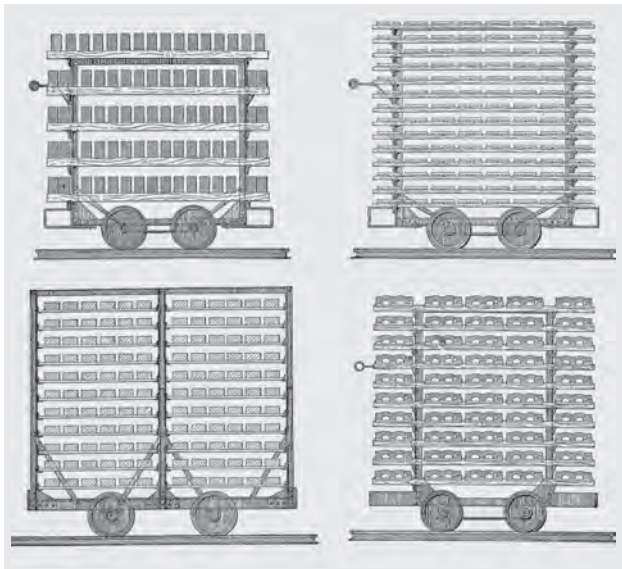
Tunneltrocknerwagen, links belegt mit Mauerziegeln, rechts mit Dachziegeln
